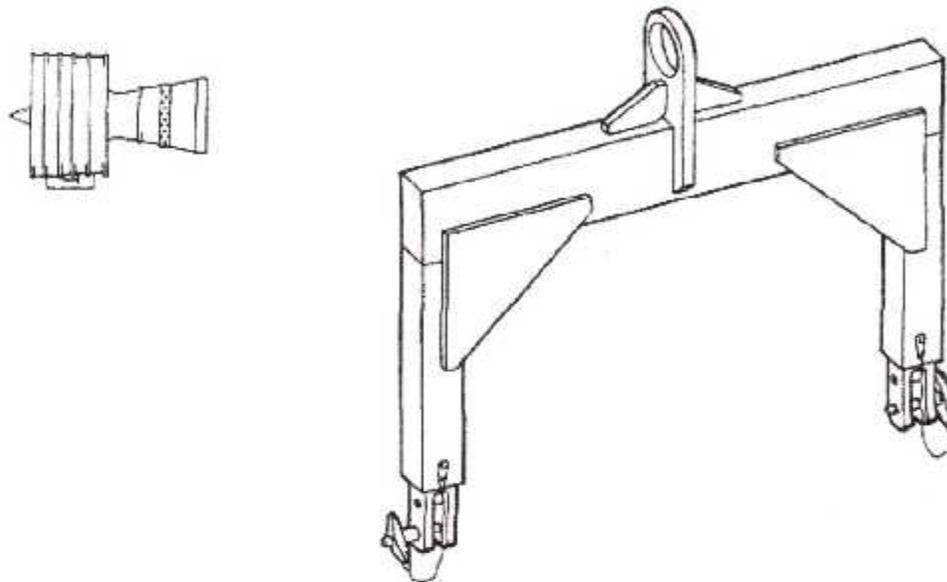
a : la Poutre de Levage et de Tour, 856A1083G02.
